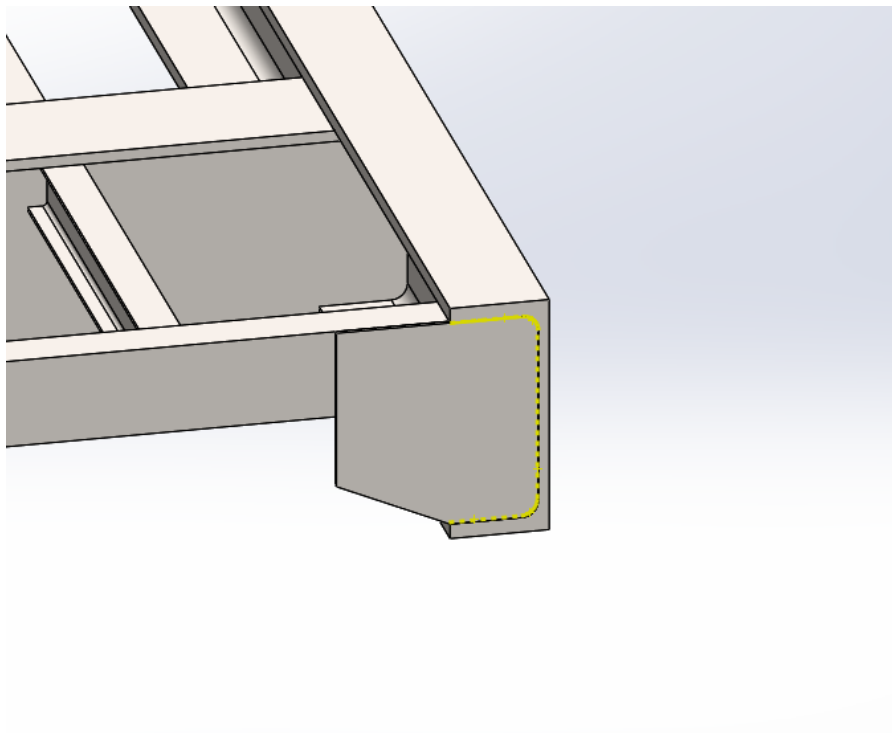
Detalle de soldadura de placa remate trasera
